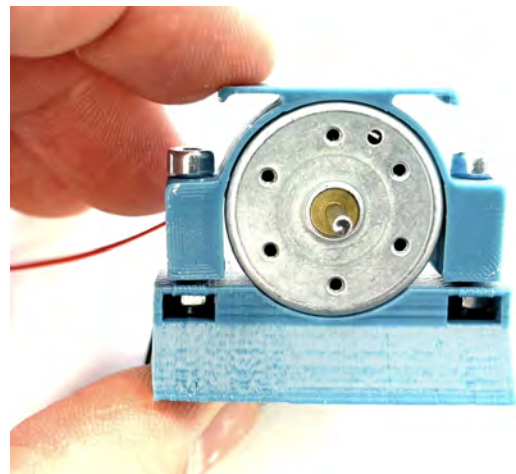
Der Klemmbügel sollte mit leichtem Druck den Motor auf dem Motorhalter fixieren.
